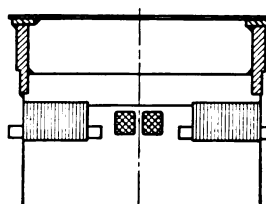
Gehäuse aus Walzstahl geschweißt für Hochfrequenzmaschinen.
